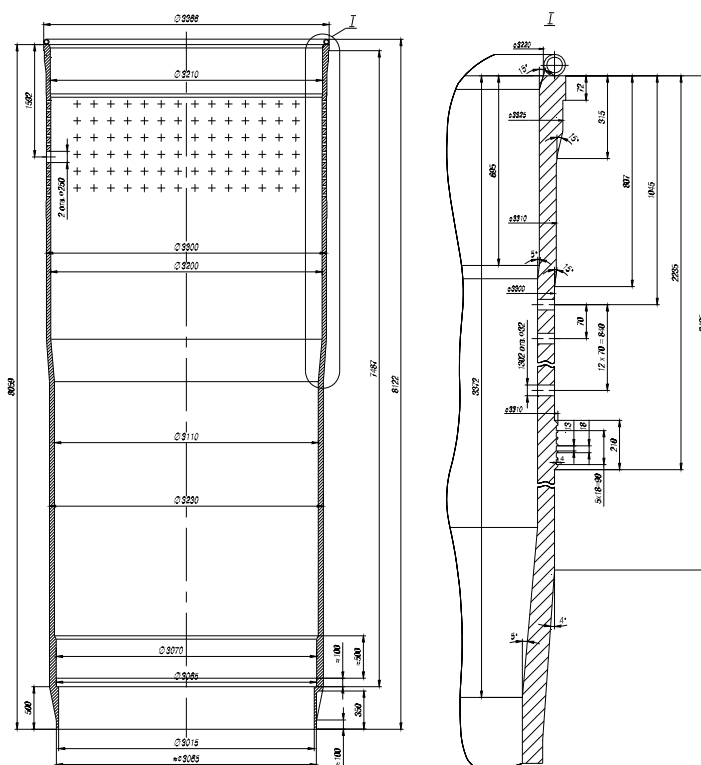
Общий вид шахты реактора ВВЭР-440 с кольцевым уплотнителем
